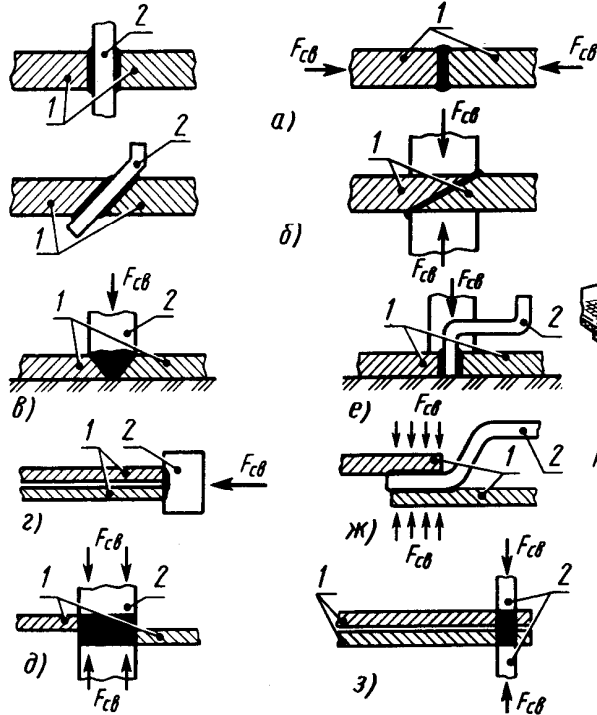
Схемы контактной тепловой сварки листовых материалов
